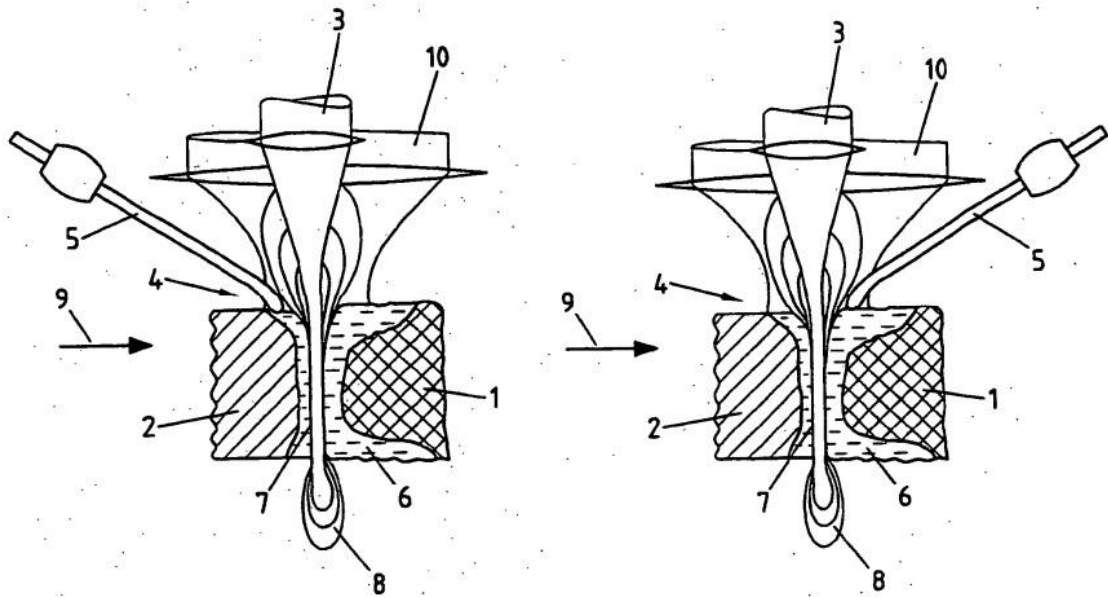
Схема двухлучевой ЭЛС с введением присадочной проволоки: 1 – сварной шов; 2 – зона соединения; 3 – луч; 4 – зона процесса; 5 – присадочная проволока; 6 – зона плавления; 7 – полость – паровой капилляр; 8 – плазма, 9 – направление движения деталей; 10 – дополнительный луч.
